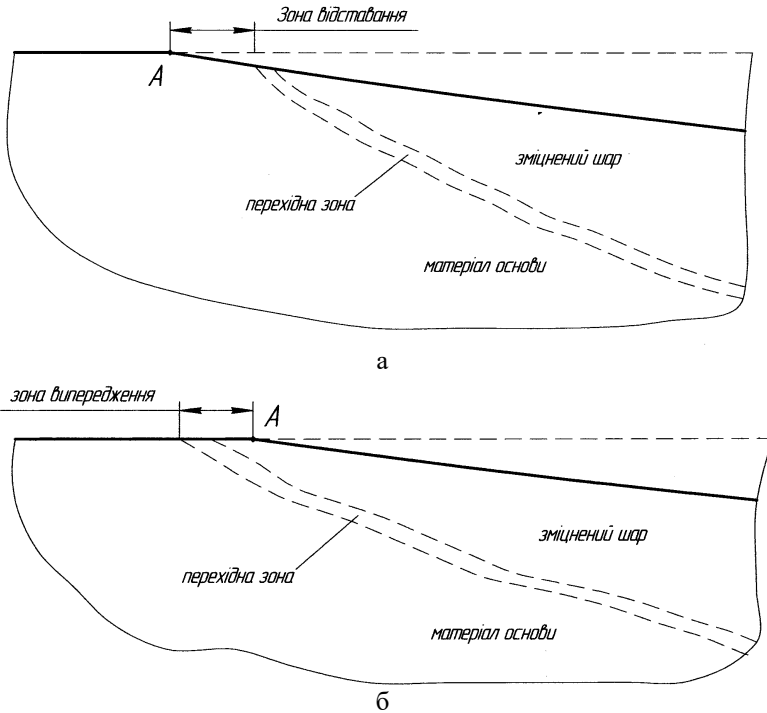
Поздовжній переріз зміцненого шару в зоні початку плями контакту інструмента-диска (збільшення  $\times 100$ ): а – зустрічний спосіб подачі заготовки; б – попутний
